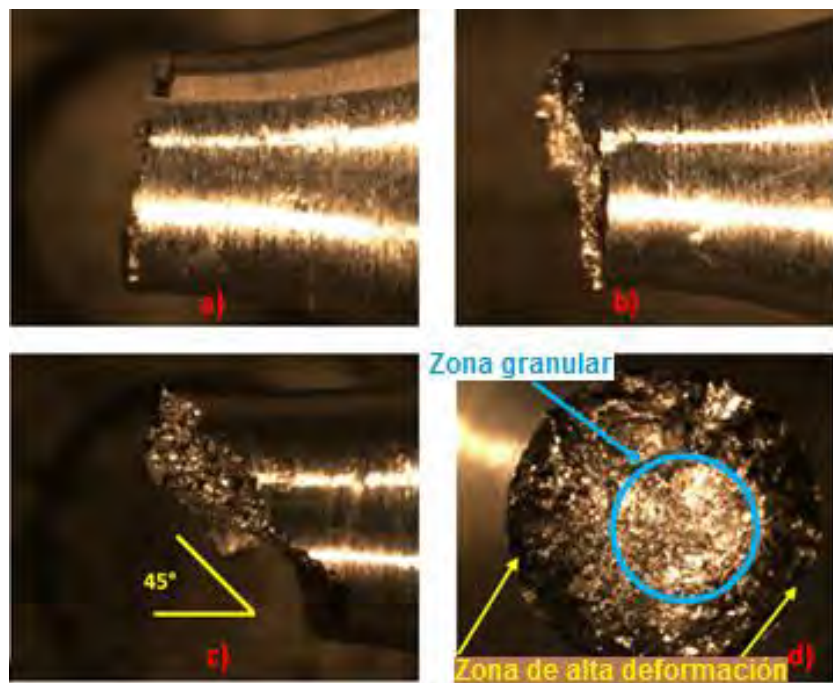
a) y b) Caminos de fractura dúctil por torsión de la aleación 6063-T5; c) vista lateral de fractura frágil y d) superficie frontal de fractura de la aleación de aluminio 6061-T6.
